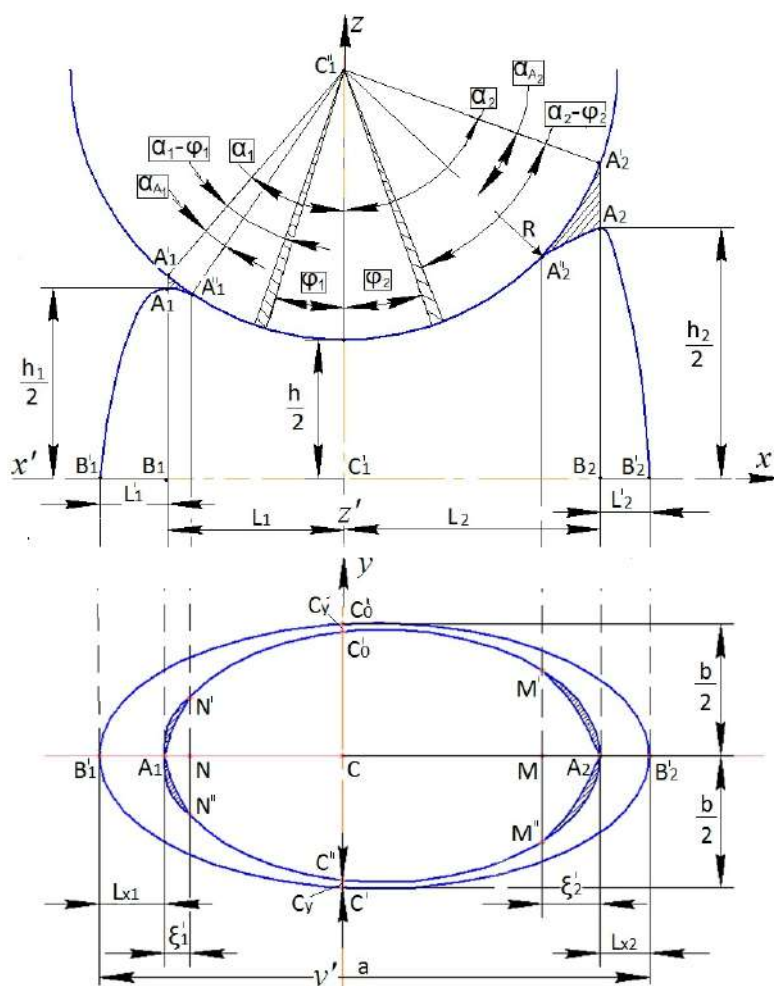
Схема асимметричной осадки цилиндрической заготовки
